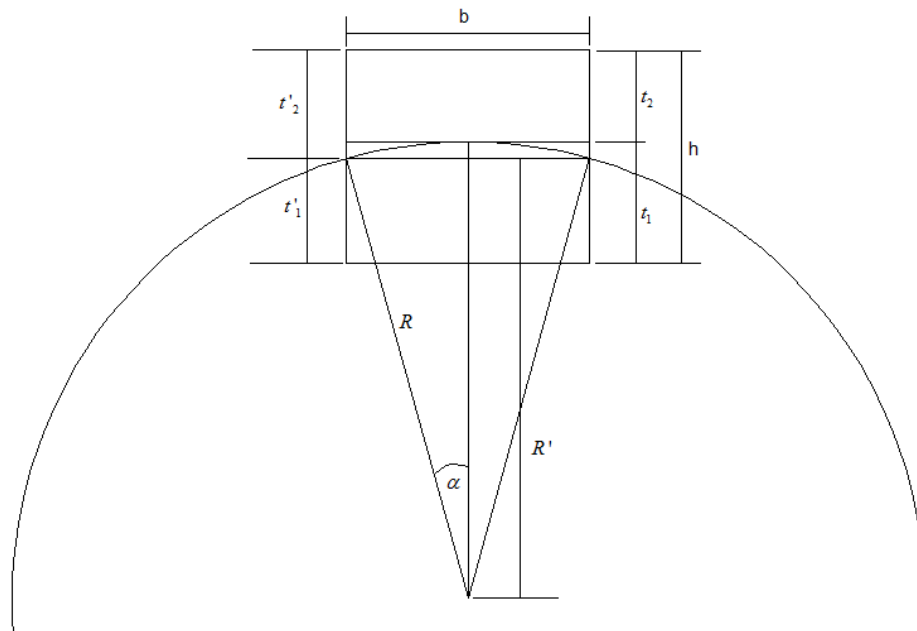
Esquema de las dimensiones de la chaveta en el eje.
